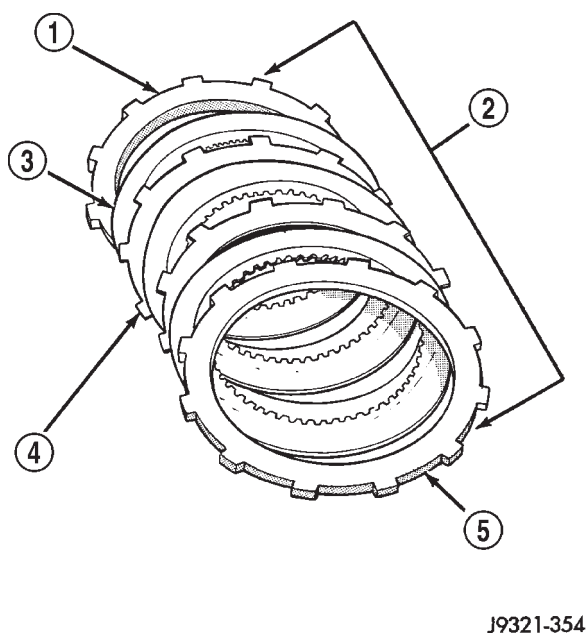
Posición de los componentes del embrague de sobremarcha 42RE
